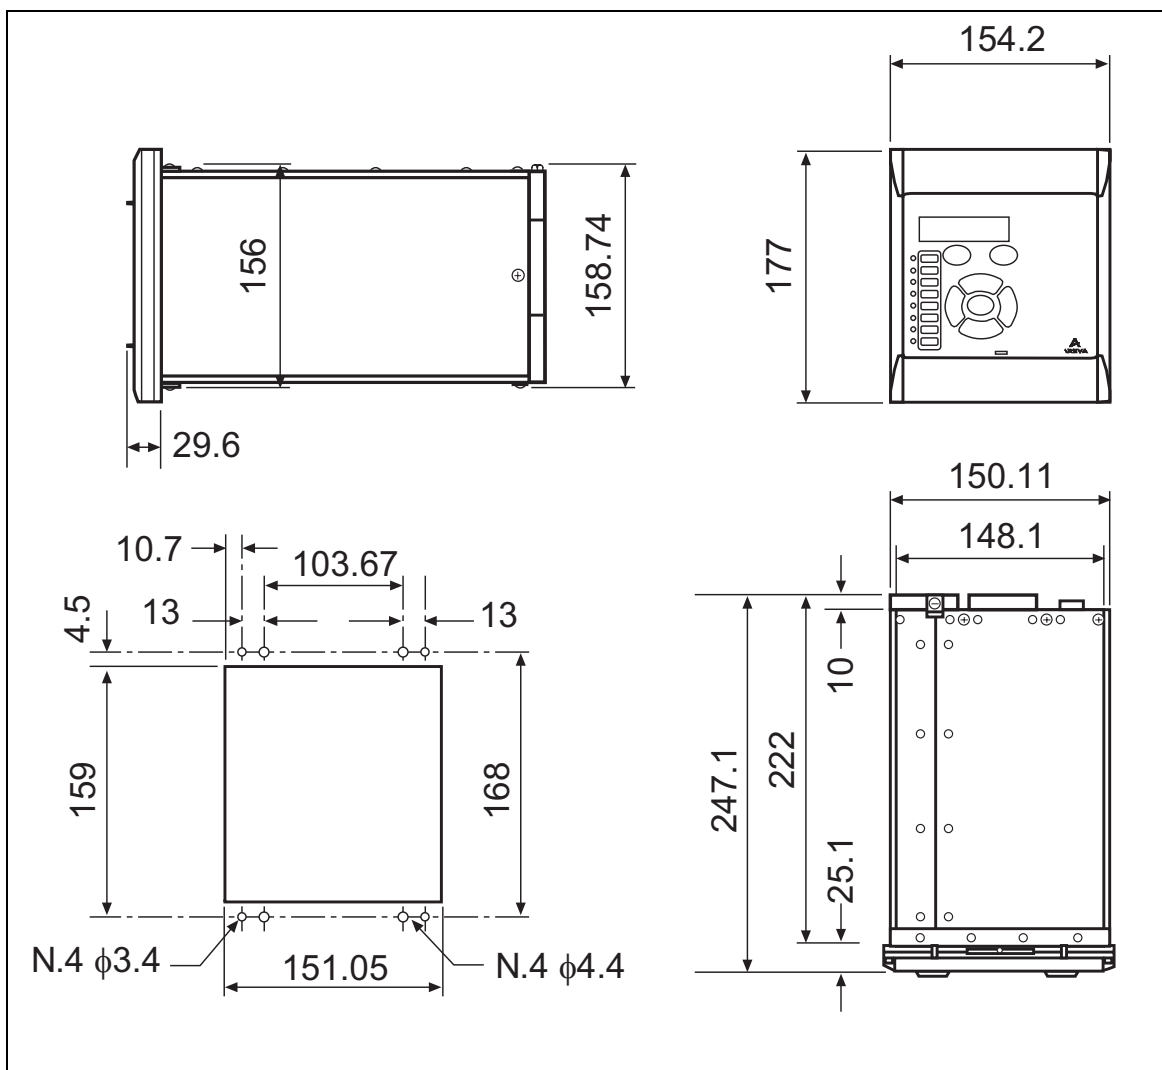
Размеры корпуса MiCOM P521 (в мм)
